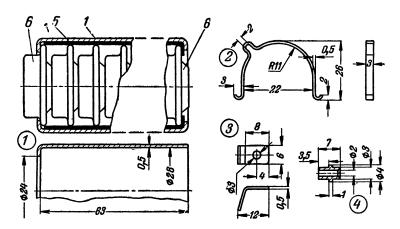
Конструкция батареи аккумуляторов и ее установочные детали.
